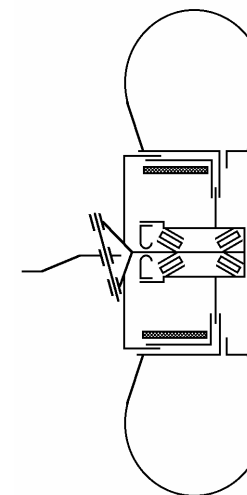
Установка переднего колеса автомобиля с колесной формулой 4×2
